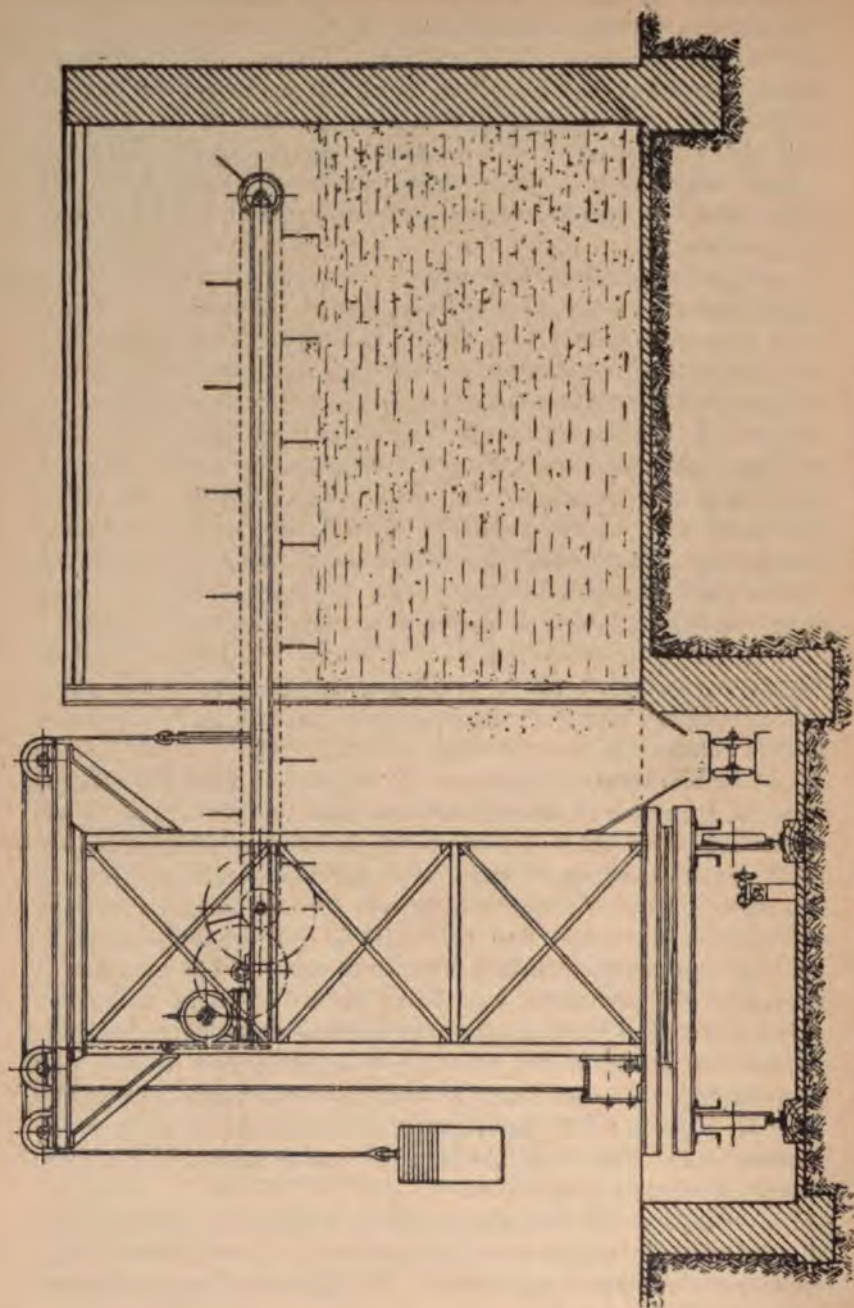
Apparecchio Keller per la vuotatura meccanica delle camere di perforato.
